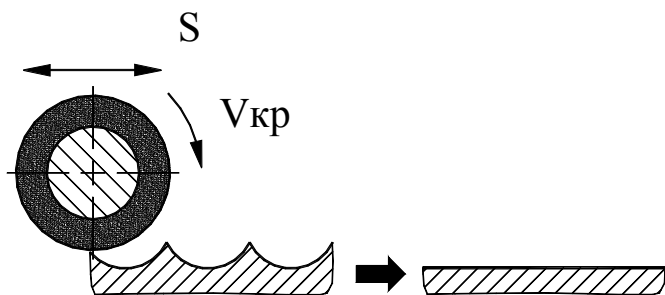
Доработка поверхностей после объемного фрезерования
